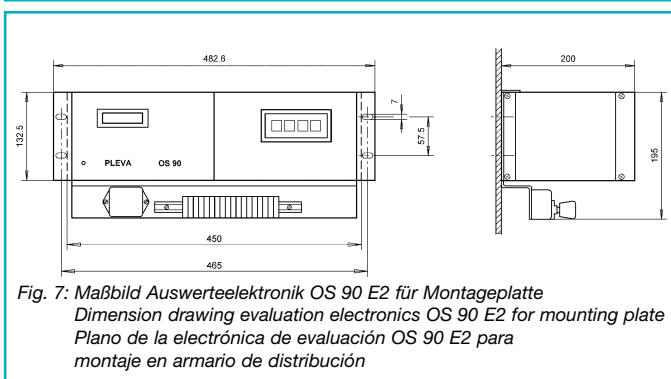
Maßbild Auswertelektronik OS 90 E2 für Montageplatte
